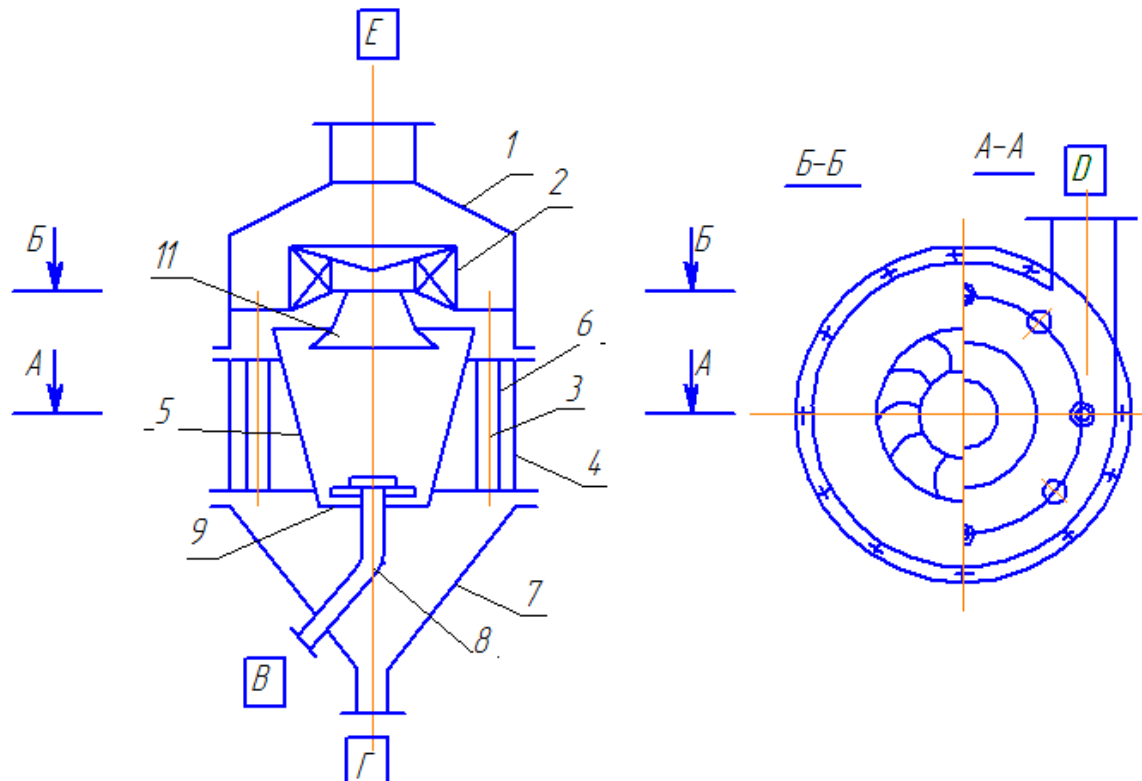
Центробежно-барботажный аппарат: 1 — верхняя крышка; 2 — каплеуловитель; 3 — сливные трубы; 4 — вихревая камера; 5 — перфорированный обратно усечённый конус; 6 — переточные трубы; 7 — коническое днище; 8 — подводящая труба; 9 — тарелка
